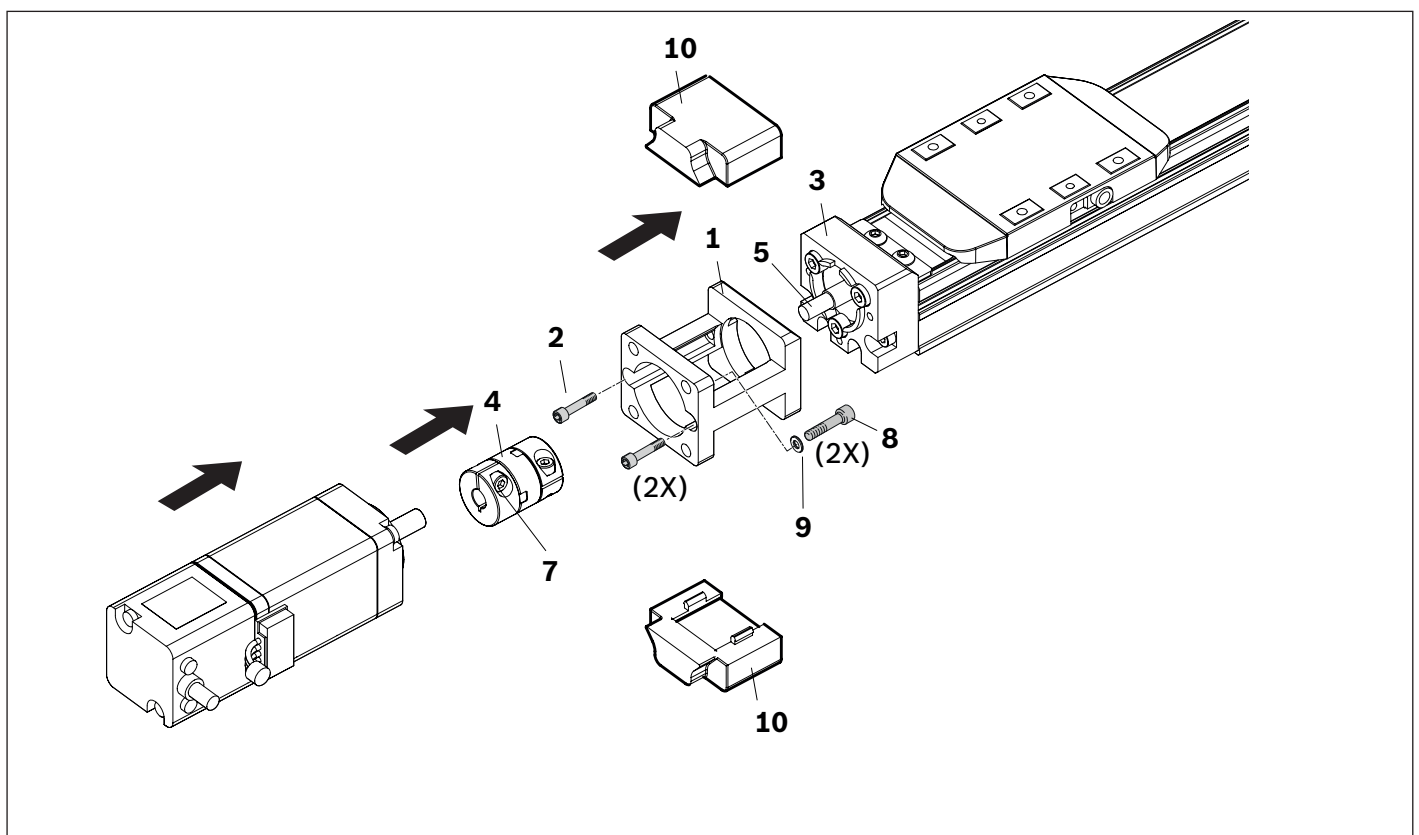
Motor mit Flansch und Kupplung montieren (SMS-030)
